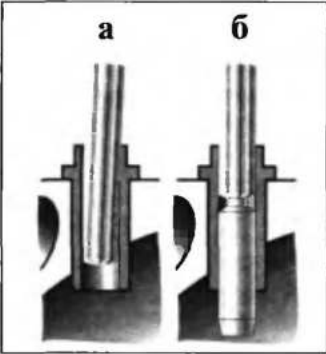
Влияние направляющей части развертки на качество ремонта отверстия (при ручном приводе развертки): а — развертка без направляющей части всегда вызывает перекос осей "нового" и "старого" отверстий; б — развертка с направляющей частью обеспечивает минимальный перекос осей
